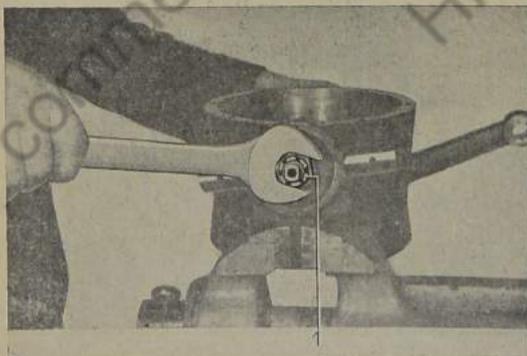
Kronenmutter vom Achsbolzen abschrauben
